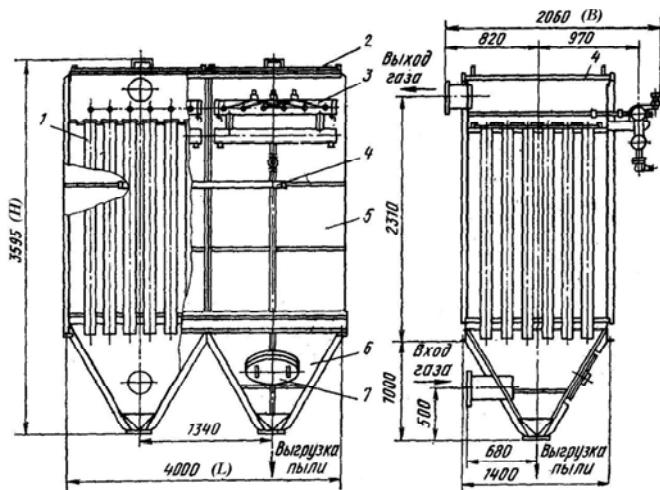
Фильтр ФРКИ (однорядный): 1 – рукав; 2 – крышка; 3 – клапанная секция; 4 – коллектор; 5 – корпус; 6 – бункер; 7 – люк
